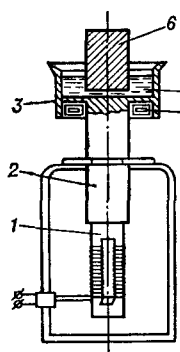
Схема установки для ультразвуковой металлизации: 1 — магнитоэлектрический преобразователь; 2 — волновод; 3 — ванна; 4 — нагреватель; 5 — расплавленный металл (припой); 6 — металлизированная деталь.
